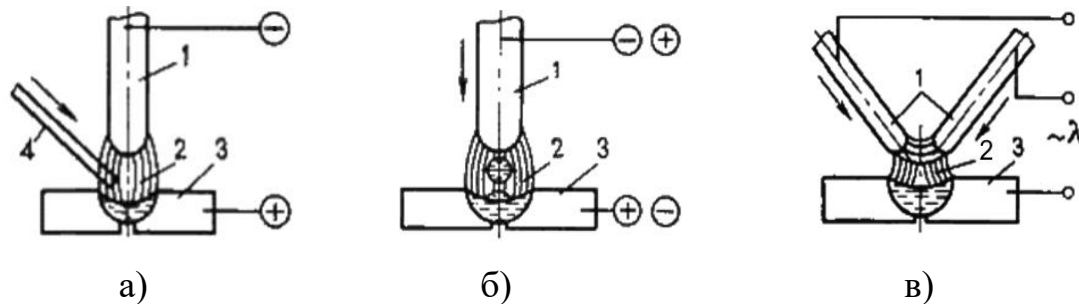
Схеми дугового зварювання: а) зварювання неплавким електродом дугою прямої дії; б) зварювання плавким електродом дугою прямої дії; в) зварювання трьохфазною дугою
